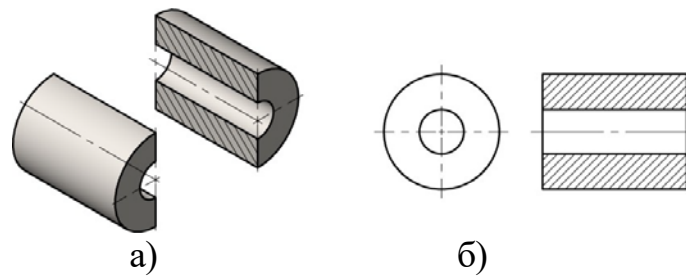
Визначення форми внутрішньої поверхні деталі
